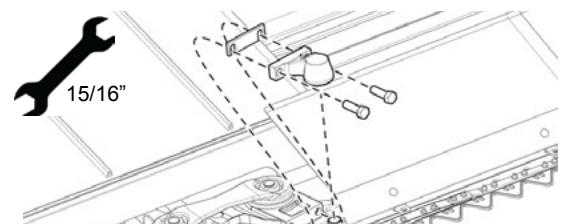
Снятие корпуса подшипников с головки левого ножа
